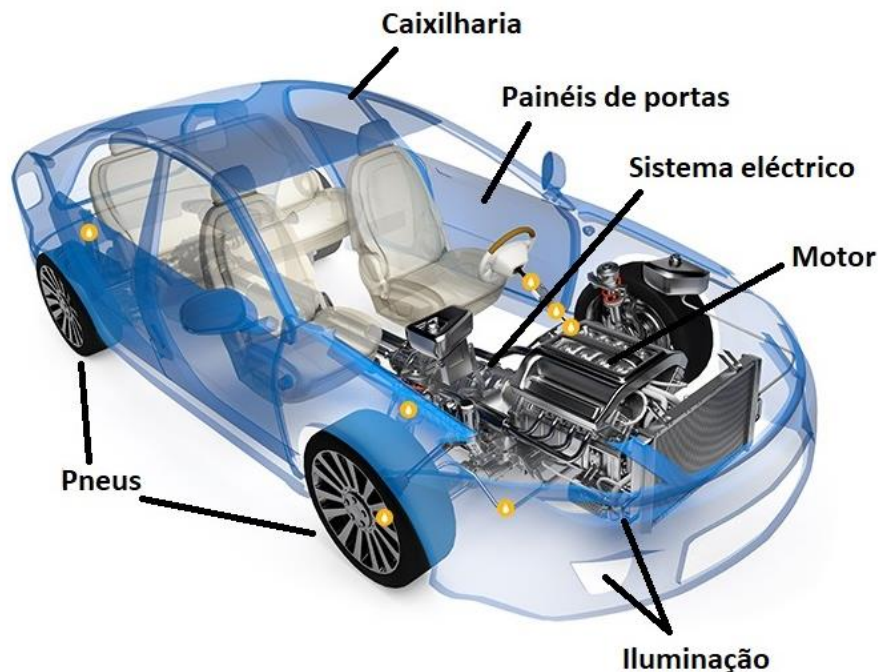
Constituição genérica de um automóvel (visão frontal) [Adaptado de (Lubricants, Chassis Components)].
